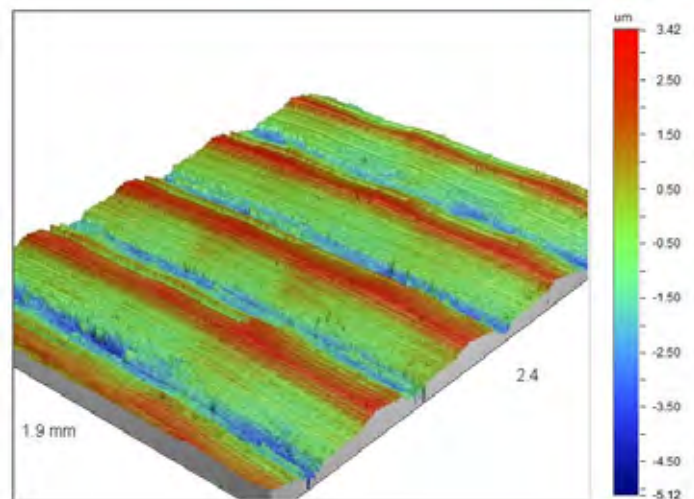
Representação tridimensional da superfície do material GUF, usinado sob condição C2.
